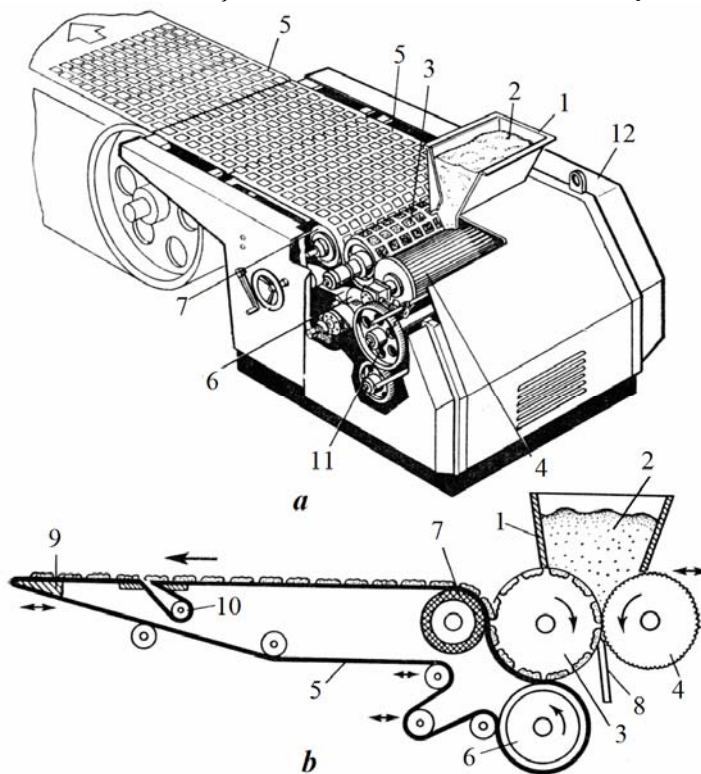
Mașina rotativă de format biscuiți zaharoși; 1- pâlnie de alimentare; 2- aluat; 3- tambur profilat; 4- tambur zimțat; 5- bandă transportoare; 6- tambur cilindric; 7- tambur elastic; 8- cuțit răzuire; 9- pană întindere; 10- rolă întindere; 11- mecanism antrenare tamburi; 12- cadru
